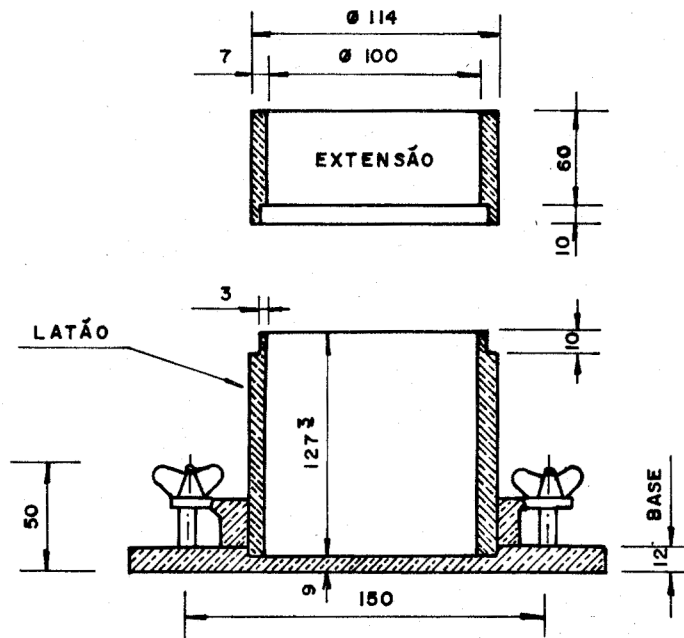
DIMENSÕES DO MOLDE METÁLICO CILÍNDRICO
